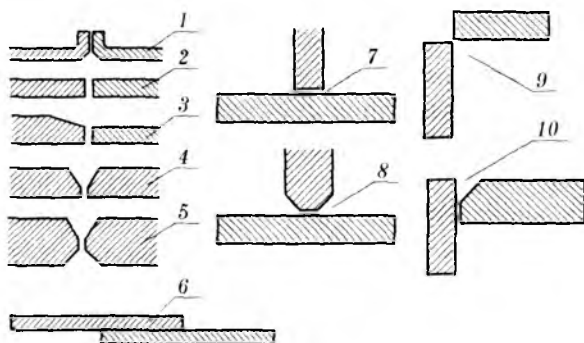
Типы сварных соединений и виды разделок кромок:
